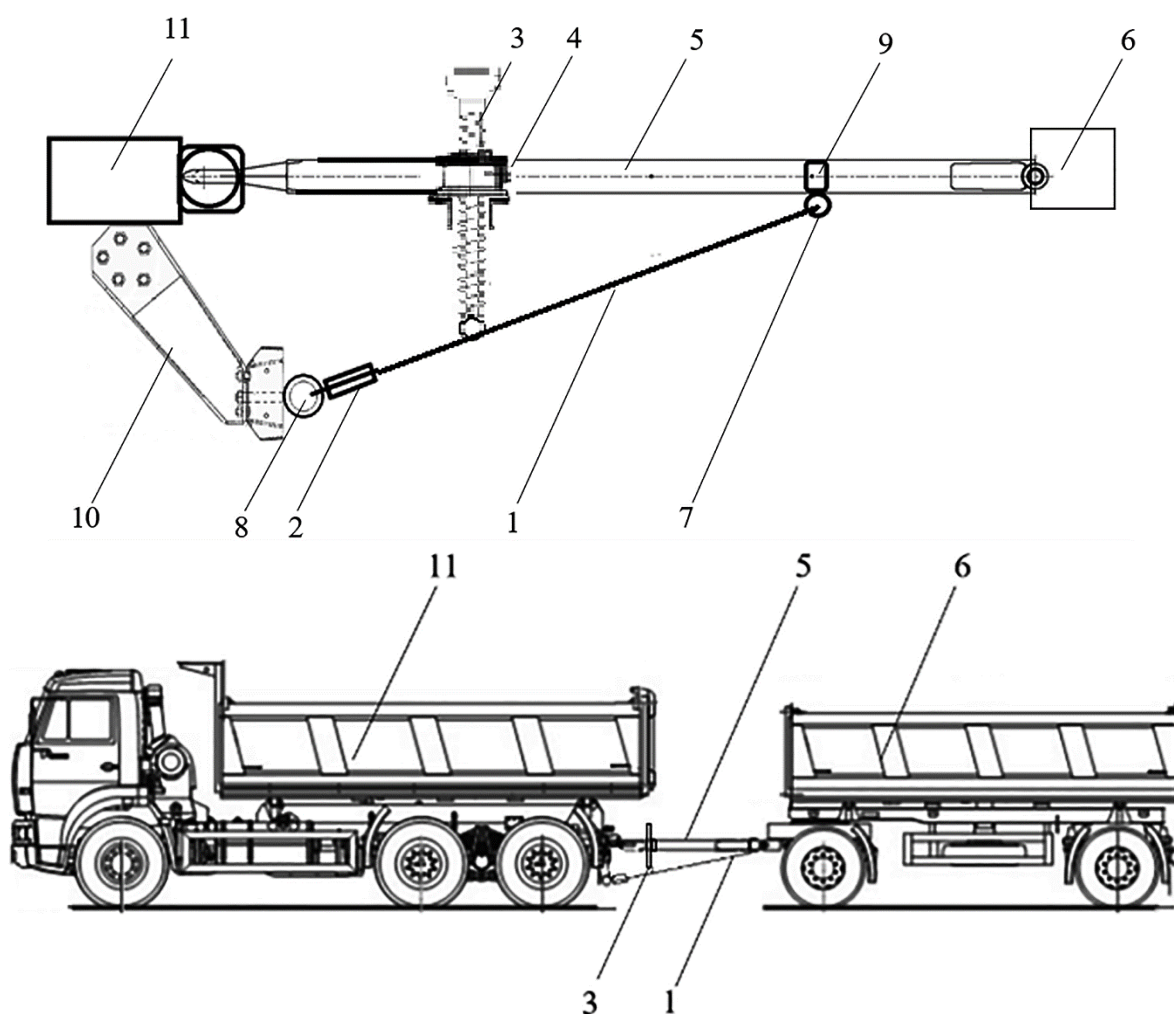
Схема установки стабилизирующего сцепного устройства одноосного прицепа на транспортном поезде
